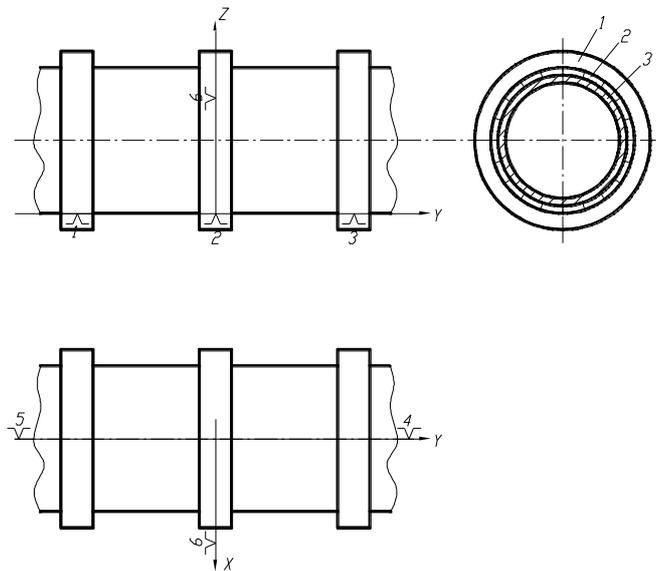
Схема базирования корпуса вращающегося агрегата:
